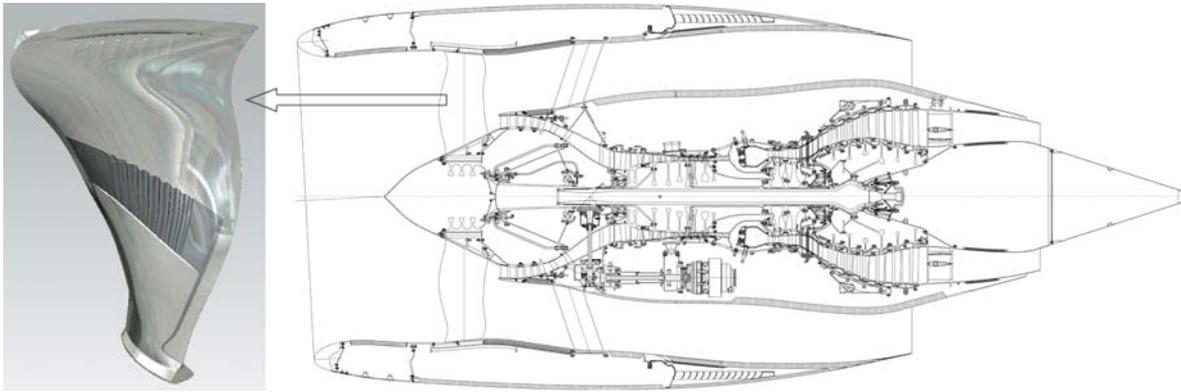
Внешний вид вентиляторной лопатки ПД-14
